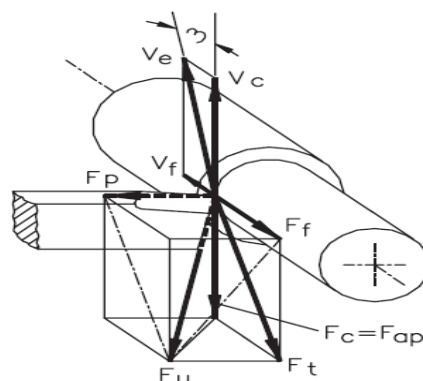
Principais componentes das forças de usinagem exercidas no processo de torneamento cilíndrico externo
